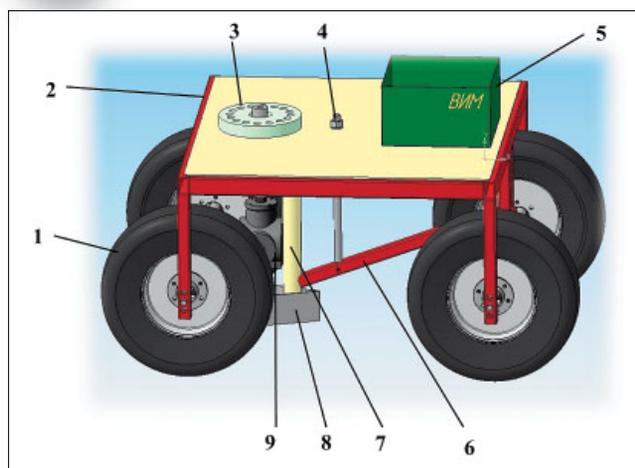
Схема экспериментального образца однорядной сеялки для посева колосьями с дисковым кассетным высевальным устройством: 1 – опорно-приводное колесо; 2 – рама; 3 – сменный кассетный диск; 4 – механизм регулирования глубины хода и подъема сошника; 5 – емкость для высеваемого материала; 6 – механизм подвески сошника; 7 – колосопровод; 8 – сошник; 9 – механизм привода ДКВУ
